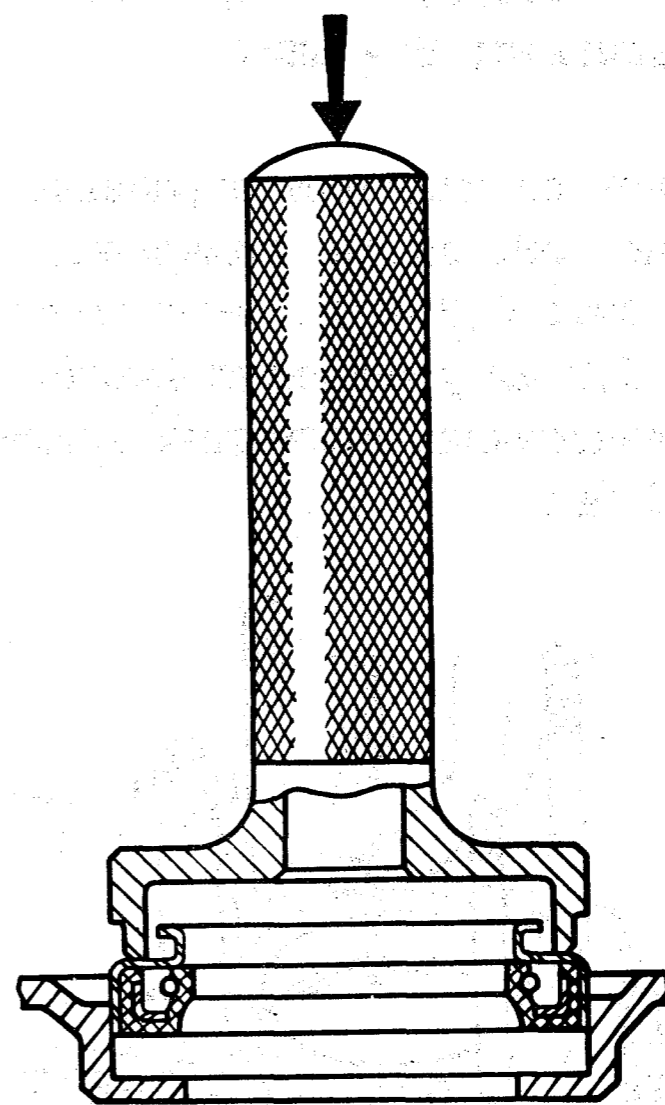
Запрессовка сальника в крышку распределительных шестерен
